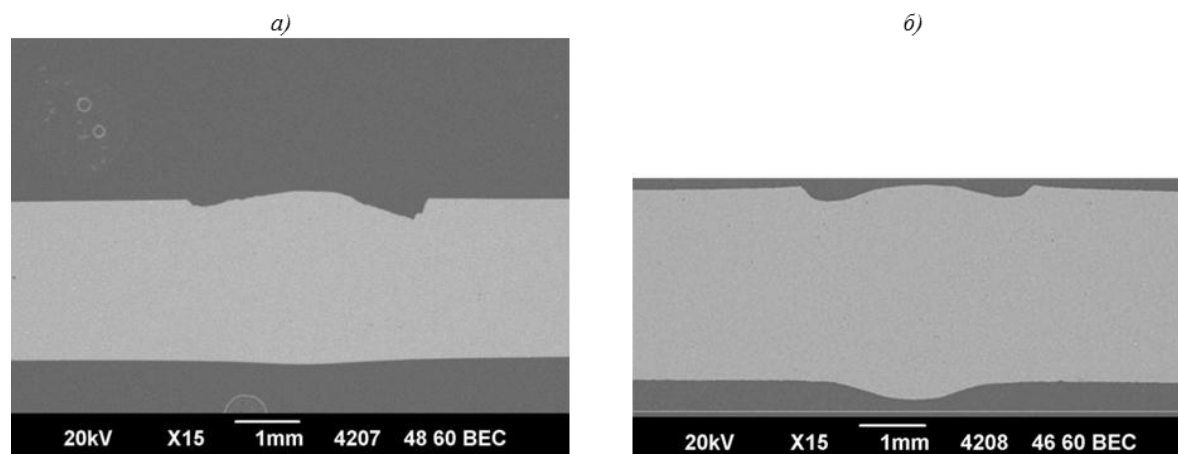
Сварной шов образцов из сплавов марок В-1579 (а) и В-1481 (б) при скорости сварки 120 м/ч
